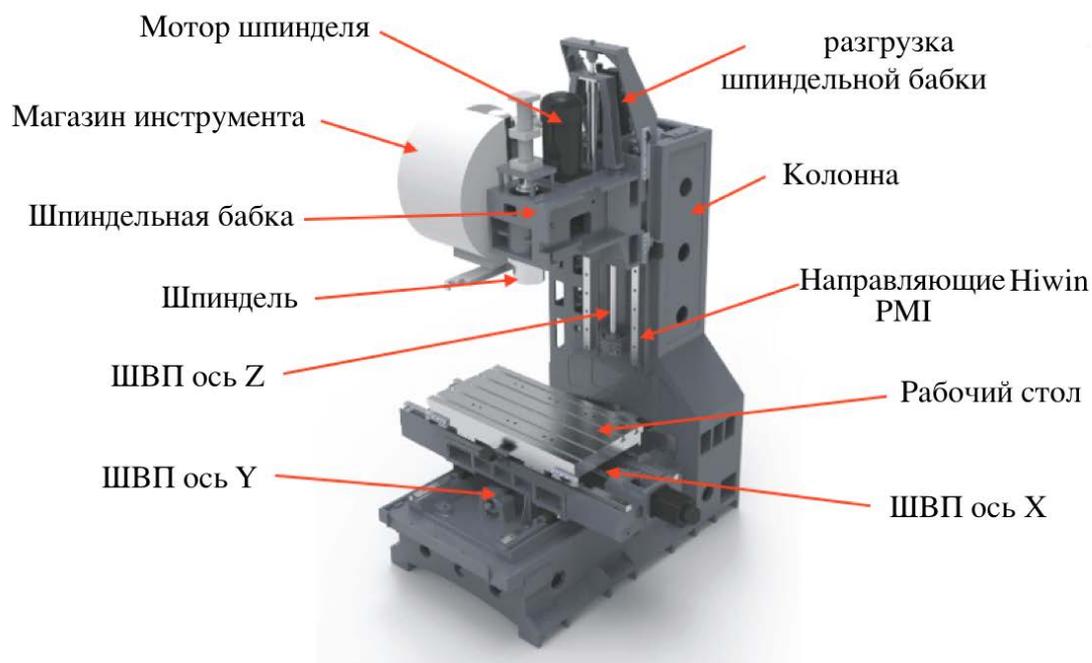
Основные узлы фрезерного обрабатывающего центра ФС65МФ3
